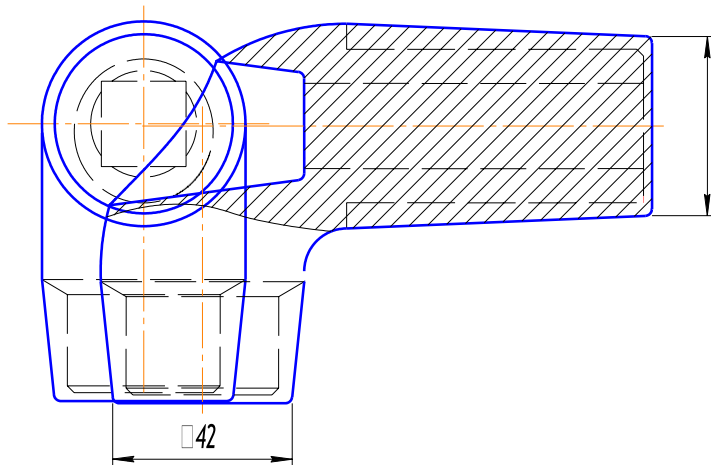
Заготовка деталі «Цапфа важель» (конструкція)
